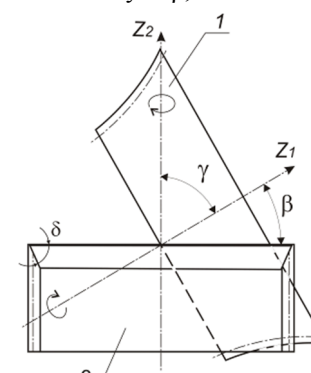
Схема изготовления квазиглобоидного колеса
